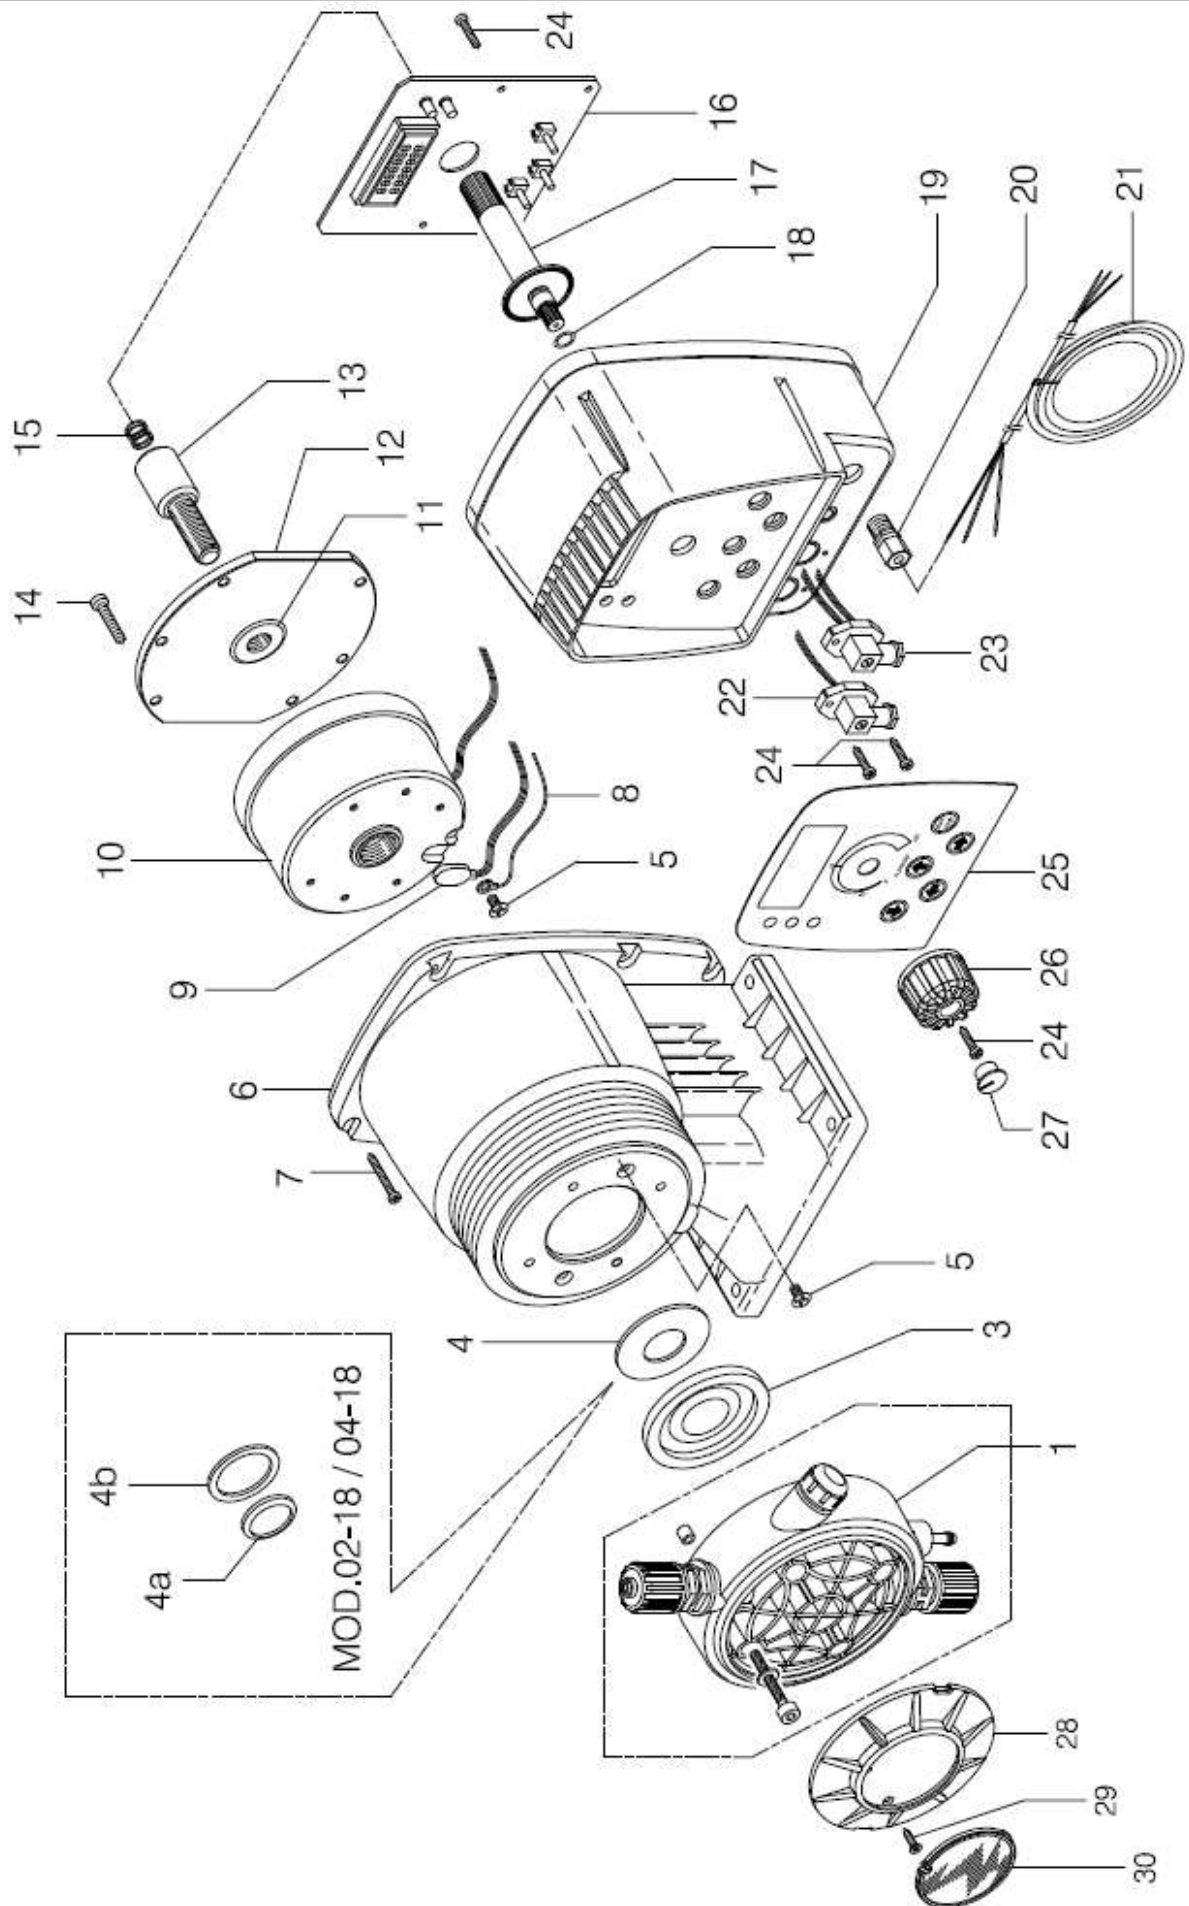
SERIE HC 1 - Esploso / Description / Explode / Dibujo / Чертеж
